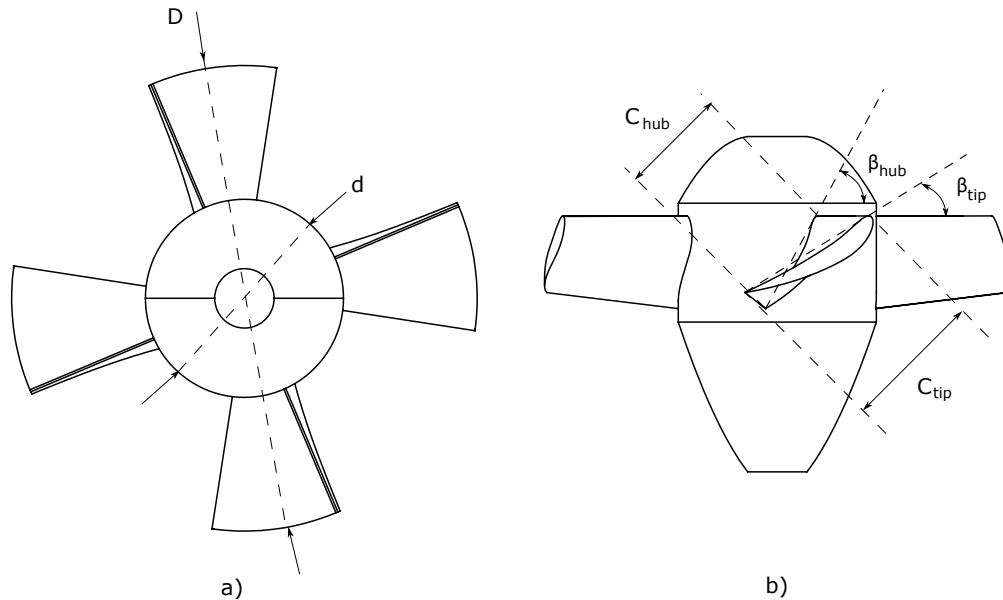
Rodete de la turbina tipo hélice: a) vista de planta y b) vista lateral.
